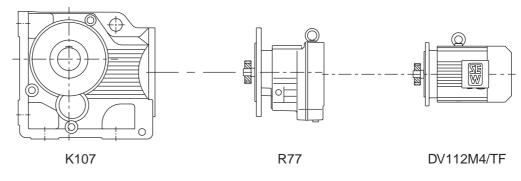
Beispiel für die Typenbezeichnung Getriebemotor
